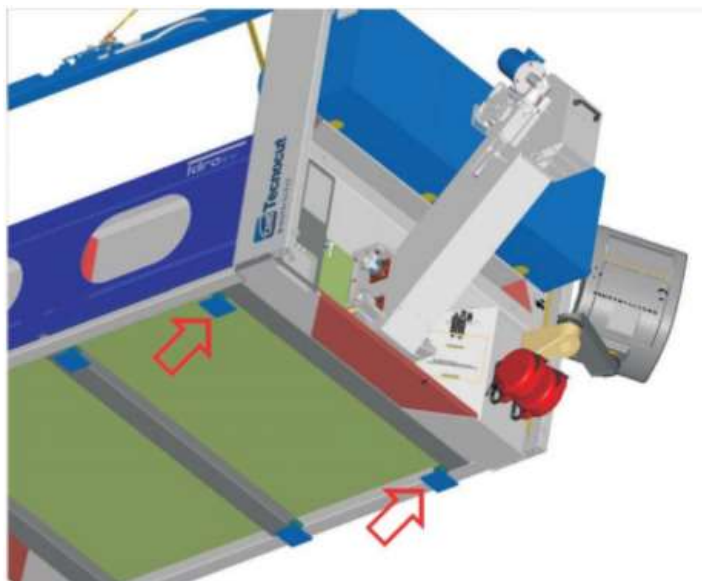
Положение винтовых опор в конструкции гидроабразивной резки
